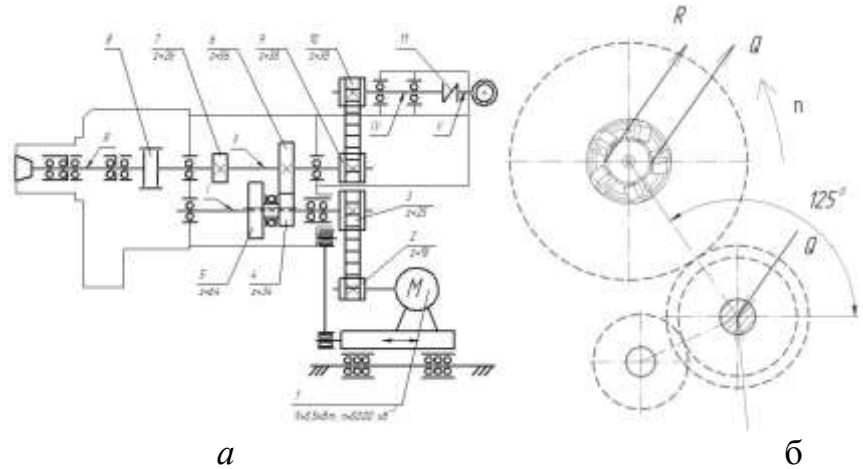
Привод главного движения ОЦ: а – кинематическая схема; б – поперечная компоновка
